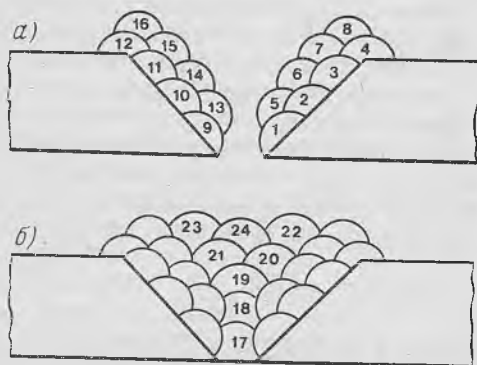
Схема сварки трещины способом отжигающих валиков:
